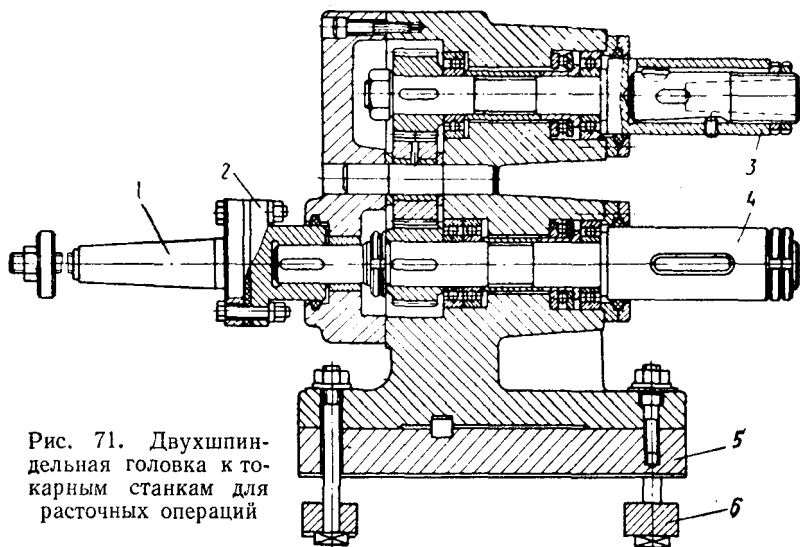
Двухшпindelная головка к токарным станкам для расточных операций
